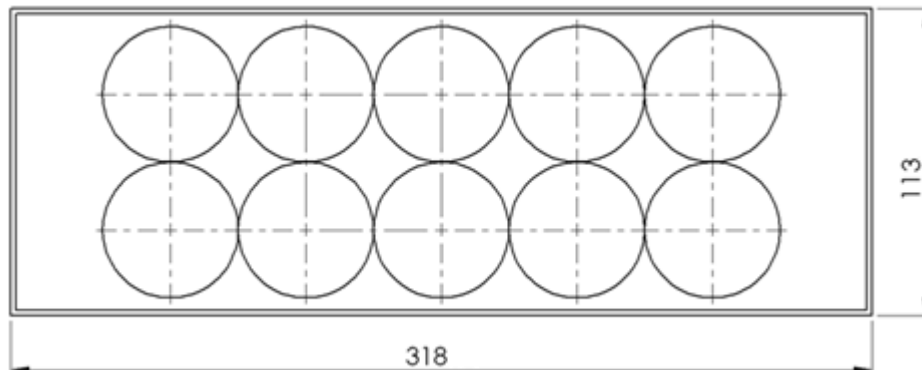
Vista en planta de la caja para cementación (cotas en mm).
